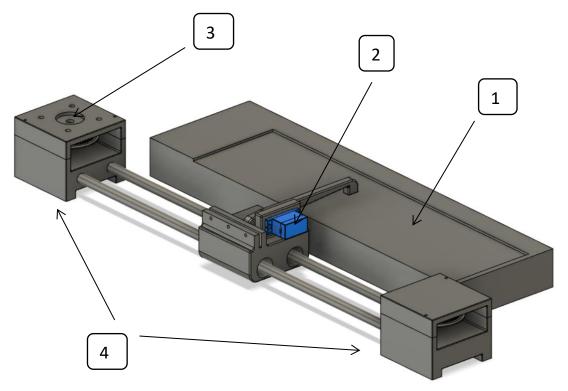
Общий вид механической части (1 - midi-клавиатура, 2 — сервопривод, 3 — место установки шагового двигателя)
